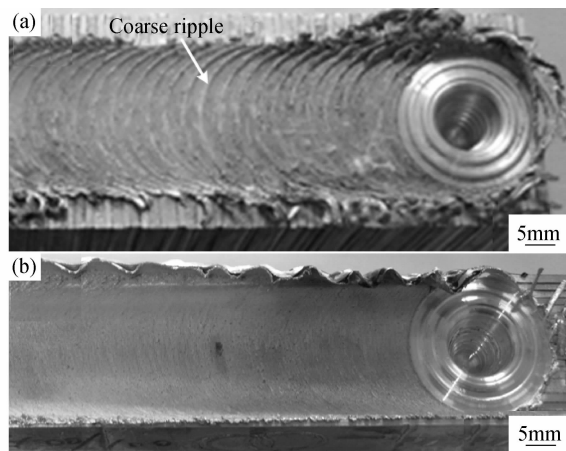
焊后试样形貌 (a)垂直焊缝排列;(b)平行焊缝排列
